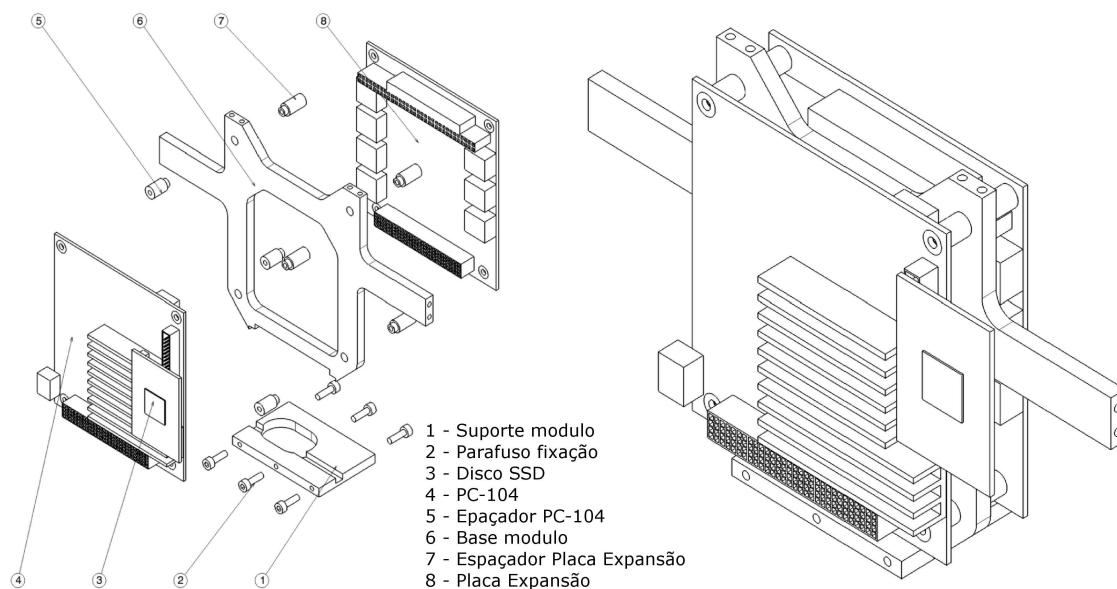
Vista explodida e de conjunto do módulo de processamento
